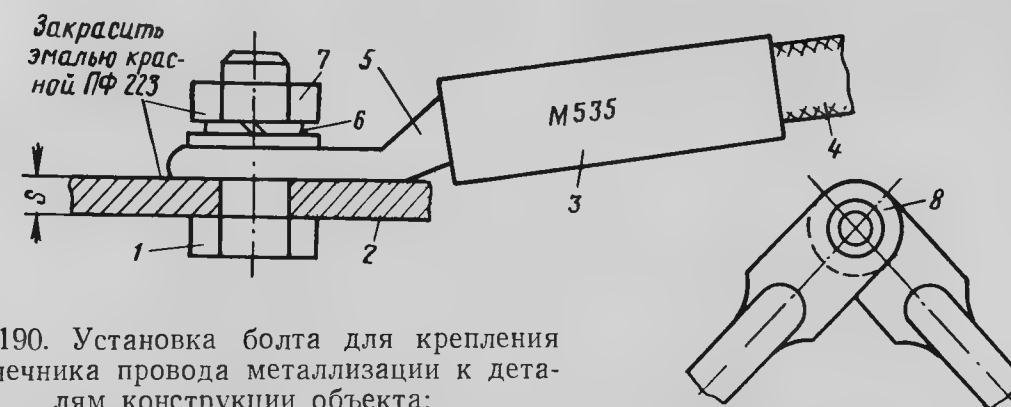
Установка болта для крепления наконечника провода металлизации к деталям конструкции объекта:
